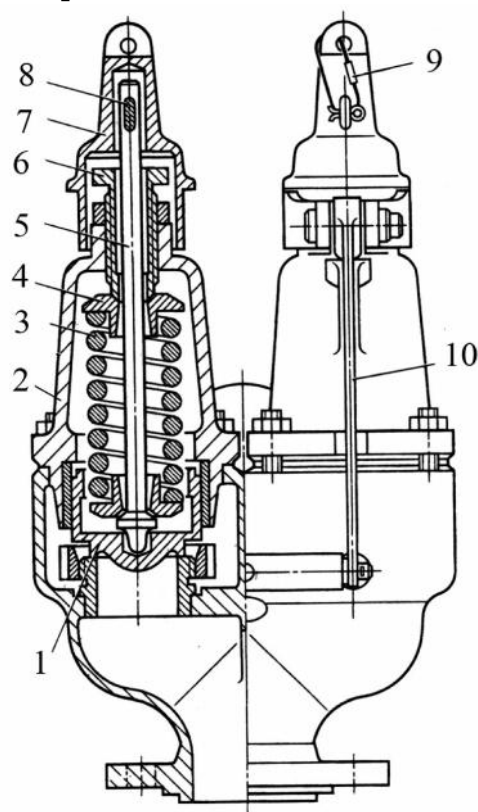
Сдвоенный предохранительный клапан: 1, 4 – тарелка; 2 – крышка; 3 – пружина; 5 – шток; 6 – втулка; 7 – колпак; 8 – чека; 9 – пломба; 10 – рычаг
